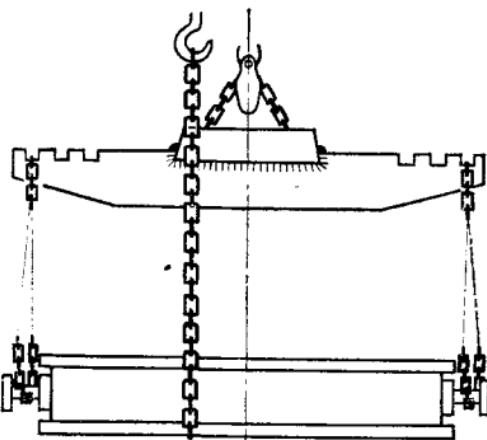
Строповка и кантовка опок, спаренных для вертикальной заливки
